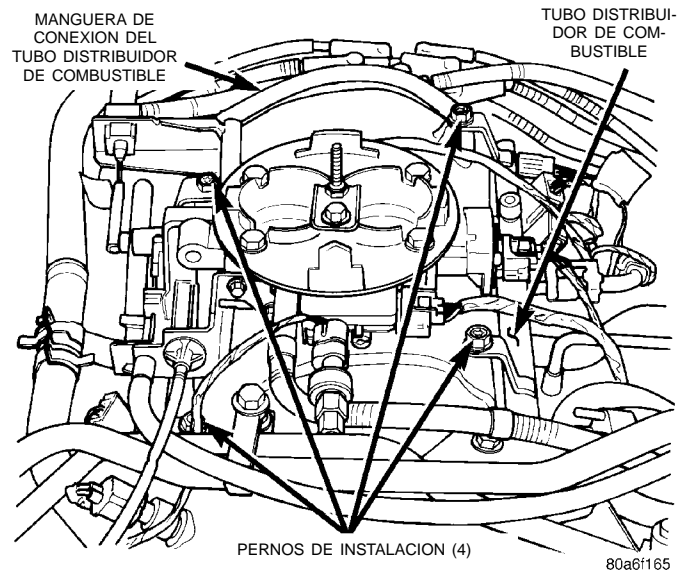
Conjunto del tubo distribuidor de combustible—Característico
